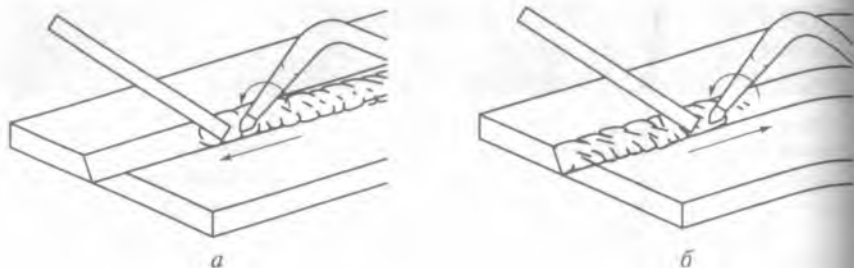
Левый (а) и правый (б) способы газовой сварки
